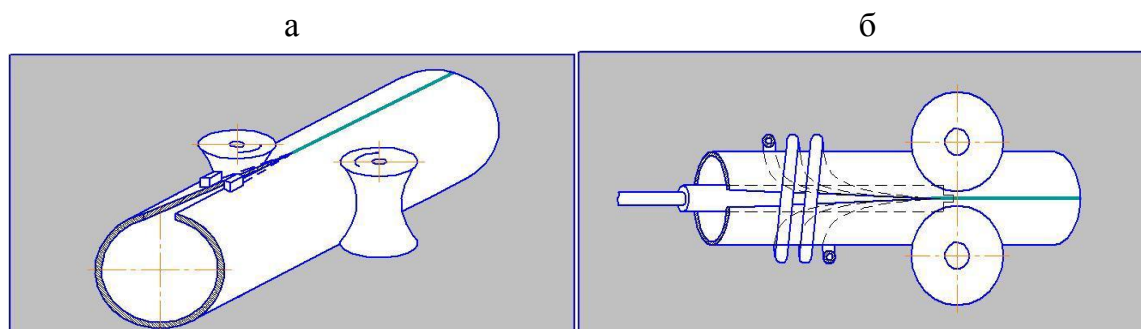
Общая схема высокочастотной сварки труб. Способы подвода электрического тока к кромкам заготовки: а- контактный, б- индукционный.
